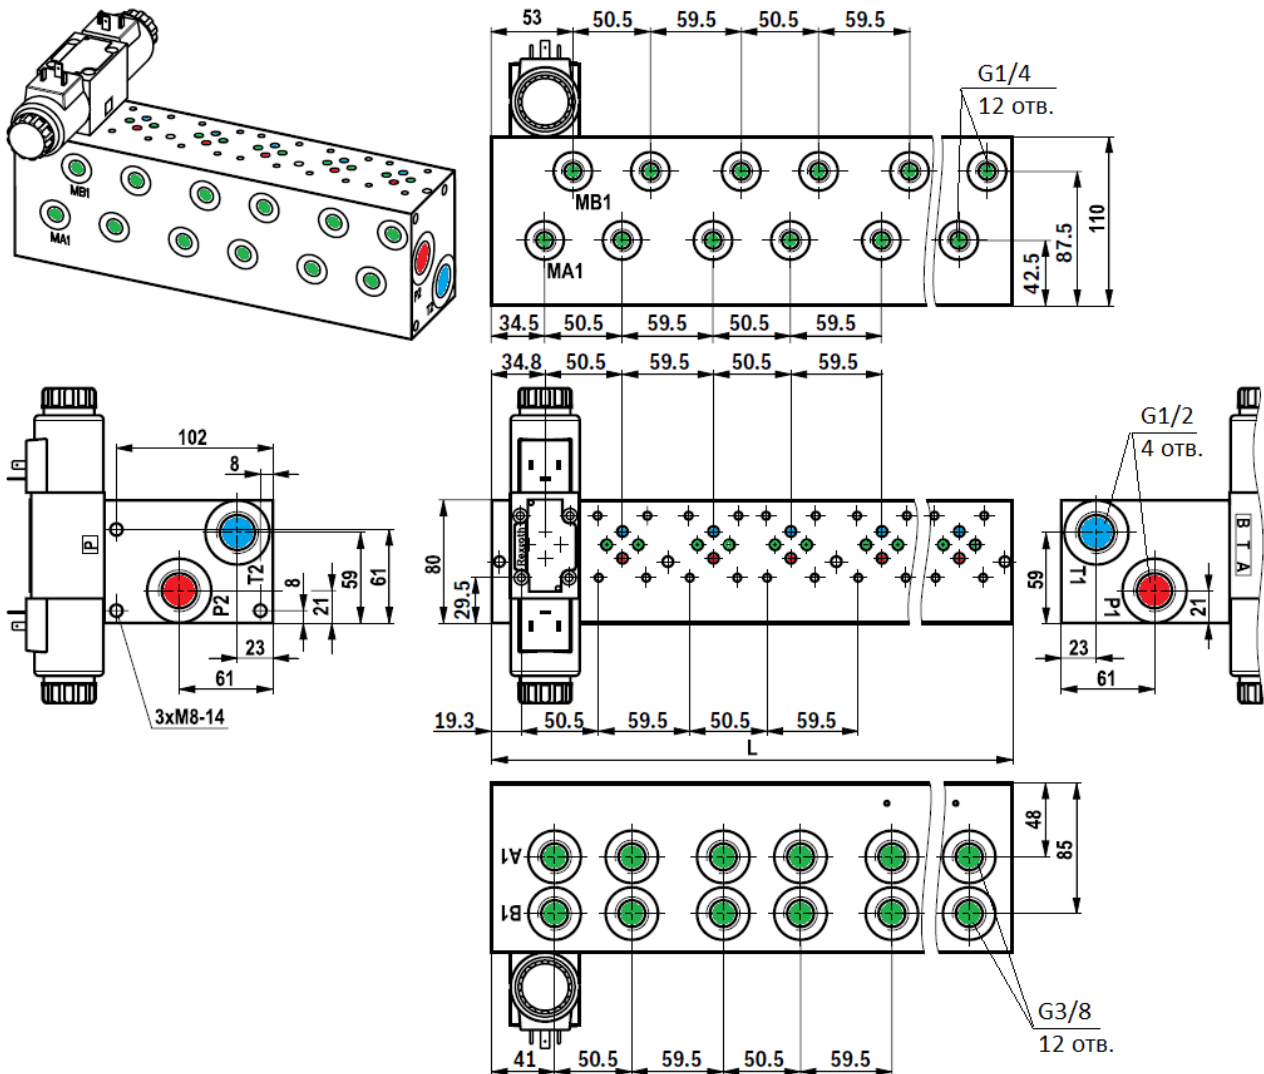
Загальний вигляд та габаритні і приєднувальні розміри багатомісної плити для гідроапаратів  $DN = 6$  мм типу HSR 06 фірми Rexroth [14]
